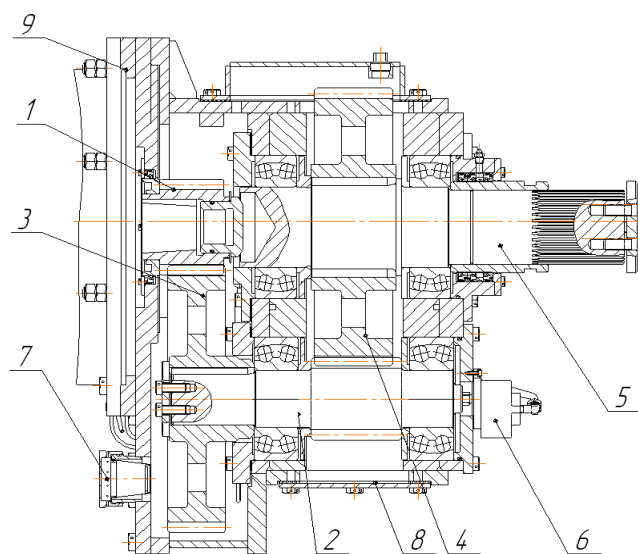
Редуктор вращателя: 1 – ведущая шестерня; 2 – вал-шестерня; 3 – зубчатое колесо; 4 – колесо; 5 – вал; 6 – крышка; 7 – сапун; 8 – шуп; 9 – фланец
